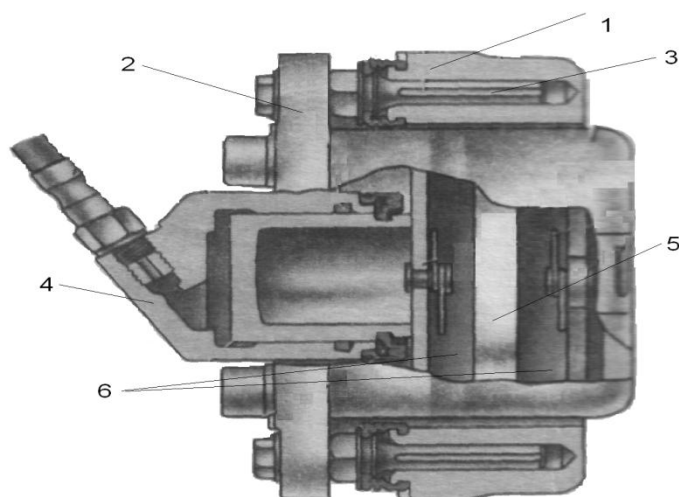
Колесный дисковый тормоз с плавающей скобой
